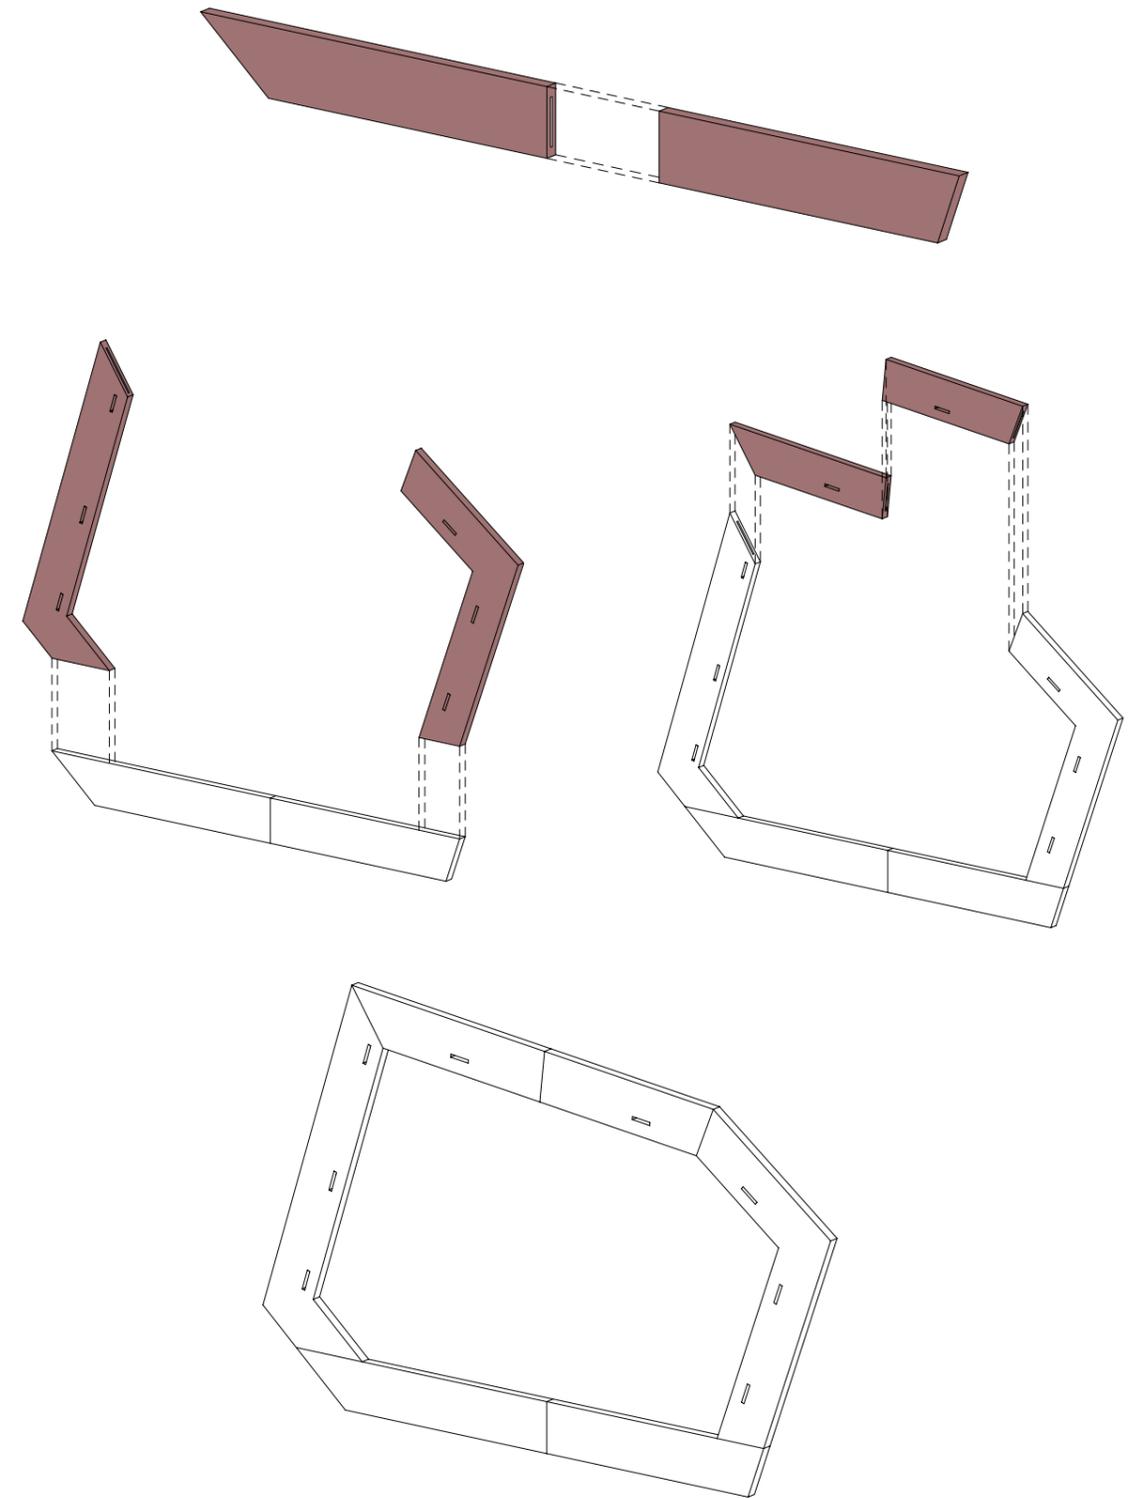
SCHEMA DI ASSEMBLAGGIO DI UNA COSTOLATURA
